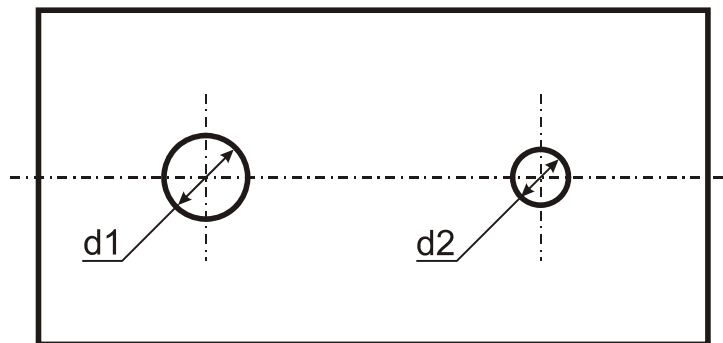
Композитная деталь образца для испытаний на податливость
